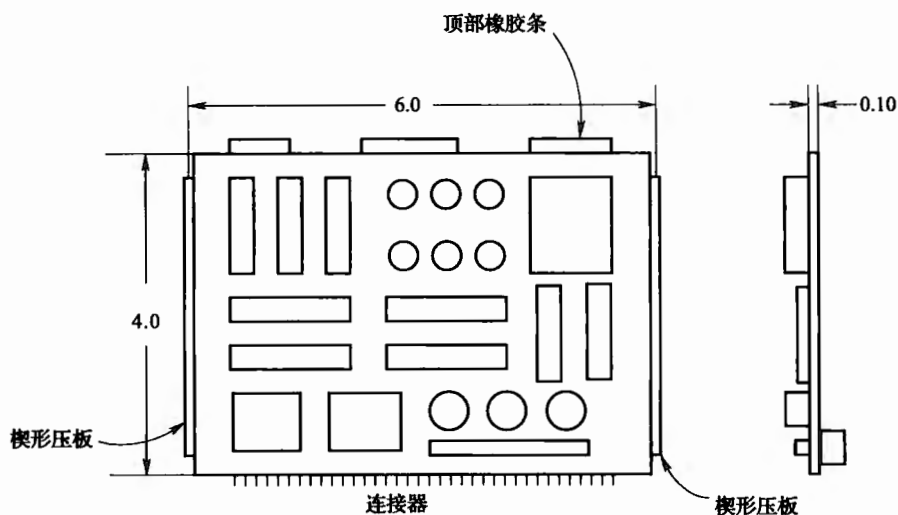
顶部和底部边缘支撑 (铰接)、侧边带楔形压板的插入式 PCB
